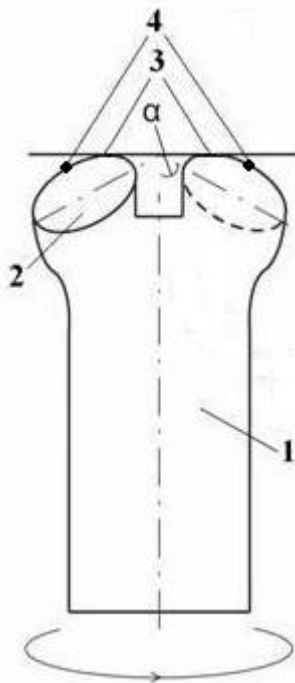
Буровой резец с режущей вставкой в форме эллипсообразного овала Кассини
